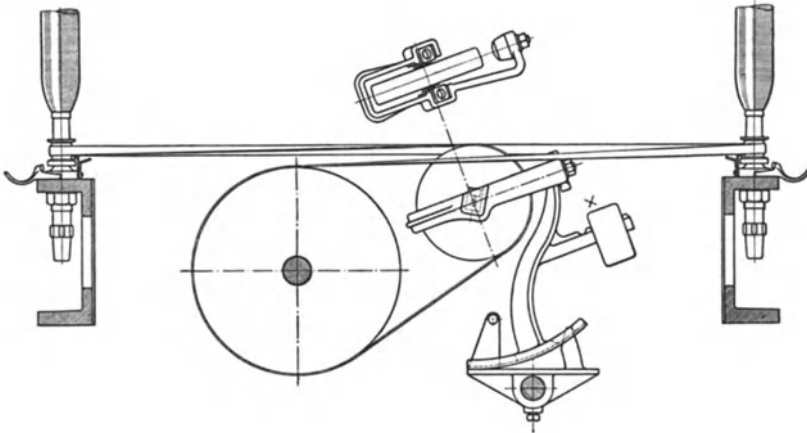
Bandantrieb für Ringspinnmaschinen (Deutsche Spinnereimaschinenbau A.-G., Ingolstadt).
